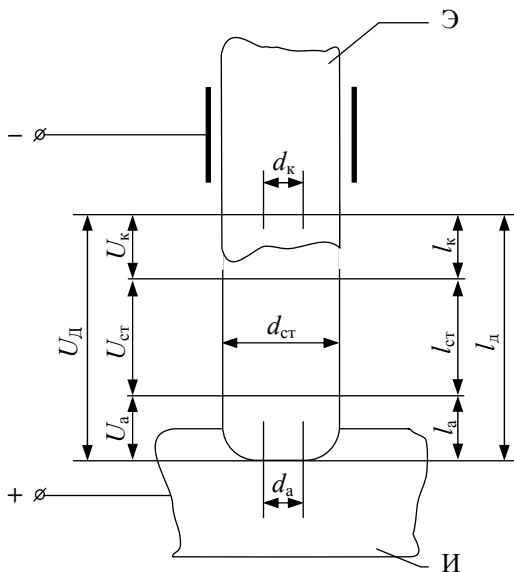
Цилиндрическая каналовая модель сварочной дуги
